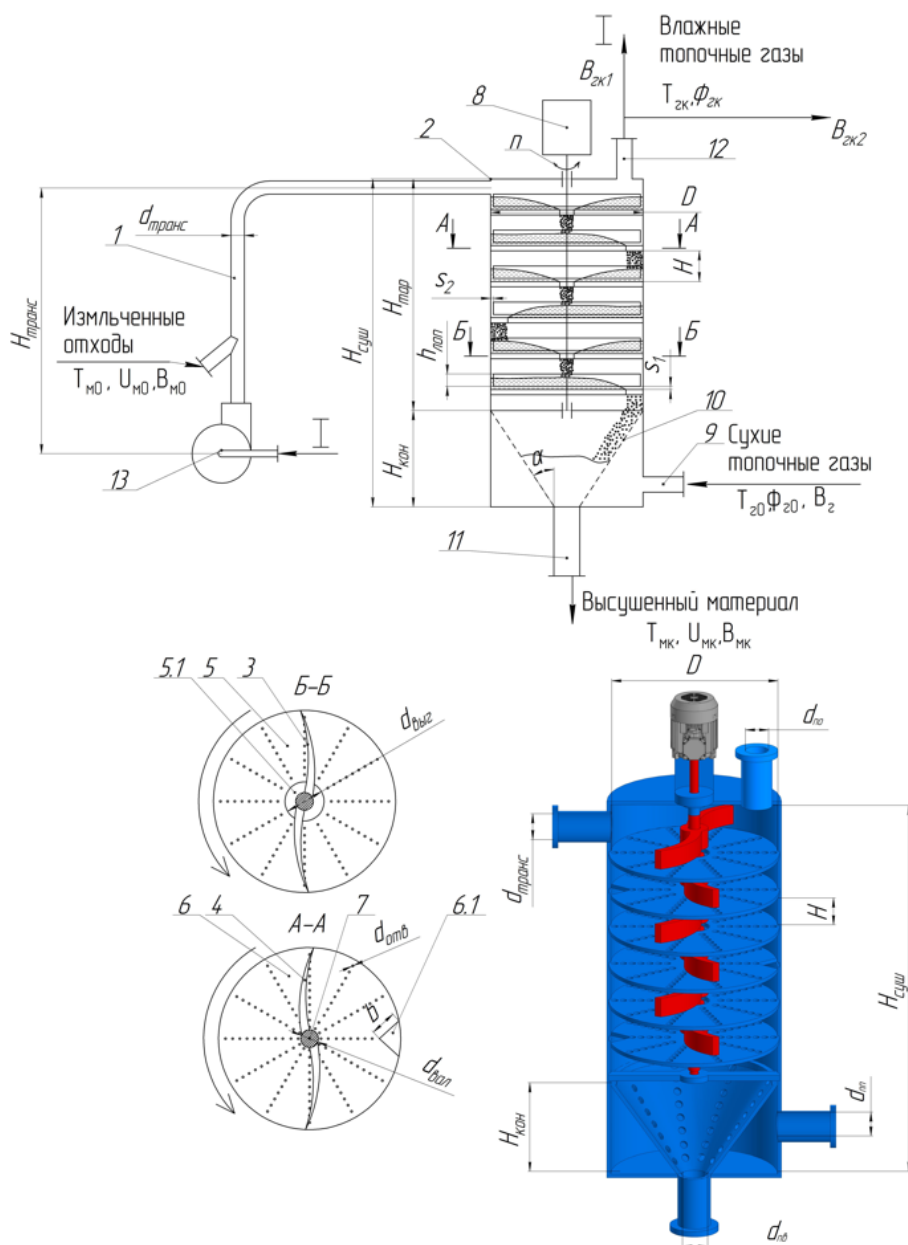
Схема и внешний вид лопастной сушилки с радиальным движением материала: 1 - пневмотраспорт; 2 – камера сушки; 3,4 – S-образные лопасти; 5,6 – перфорированные тарелки; 5.1,6.1 – выгрузочные отверстия; 7 – вал; 8 – привод; 9 – патрубок подачи топочного газа; 10 – перфорированный конус; 11 – патрубок выгрузки высушенного сырья; 12 – патрубок отвода топочного газа; 13 – газодувка
